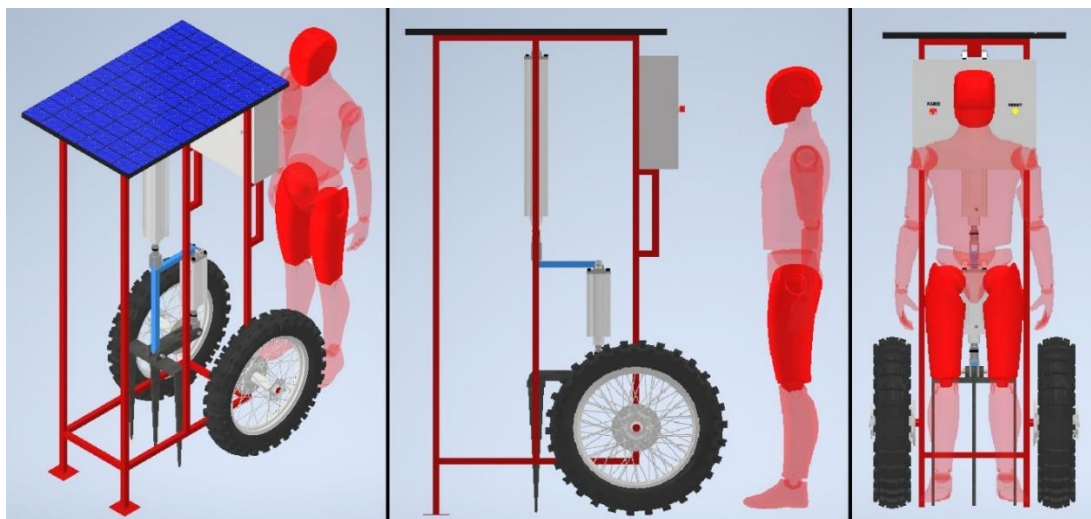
Diseño final de la máquina, se aprecia el ensamblado junto a un operador
